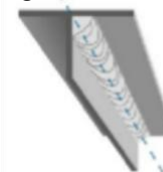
Soldadura en posición 4F (American Welding Society, 2018)
